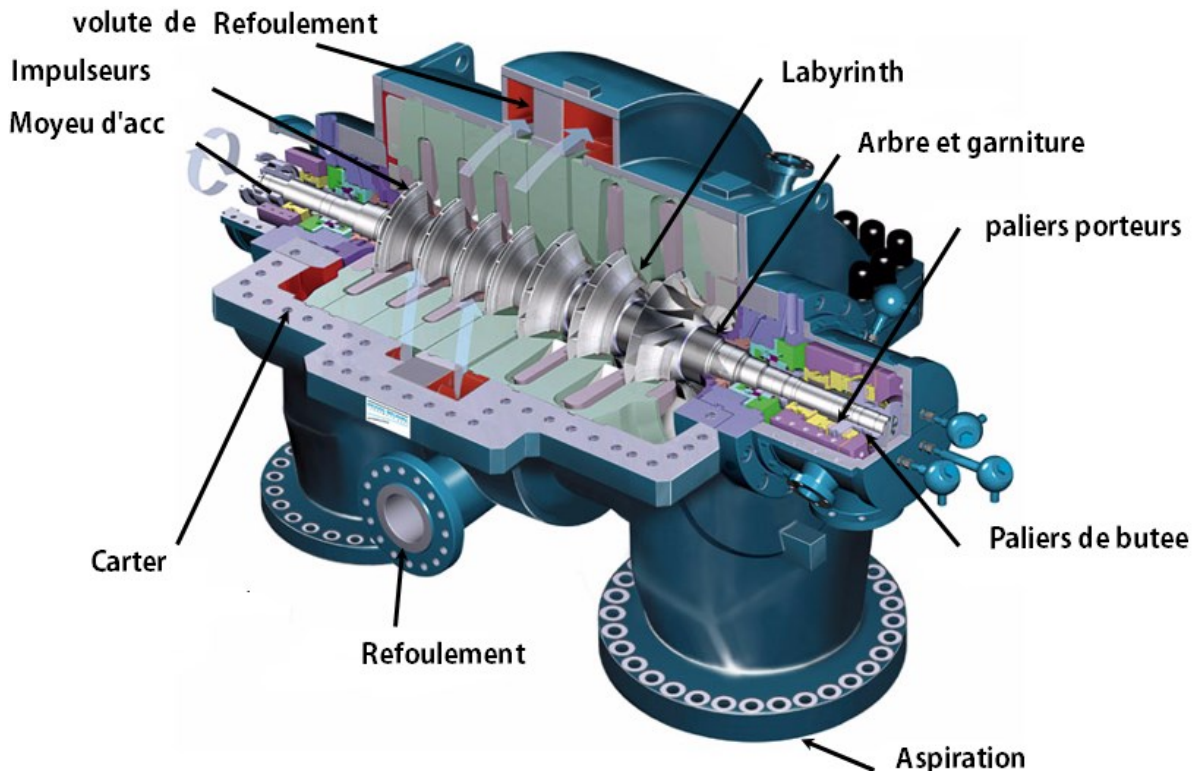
Exemple d'une machine tournante : Compresseur centrifuge à deux étages [6].
